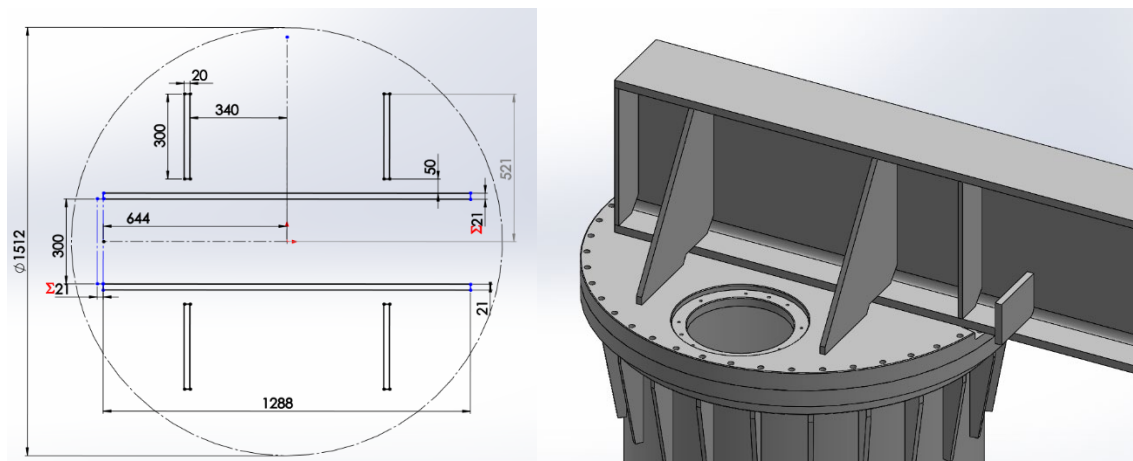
Esquema de las soldaduras de cálculo.
